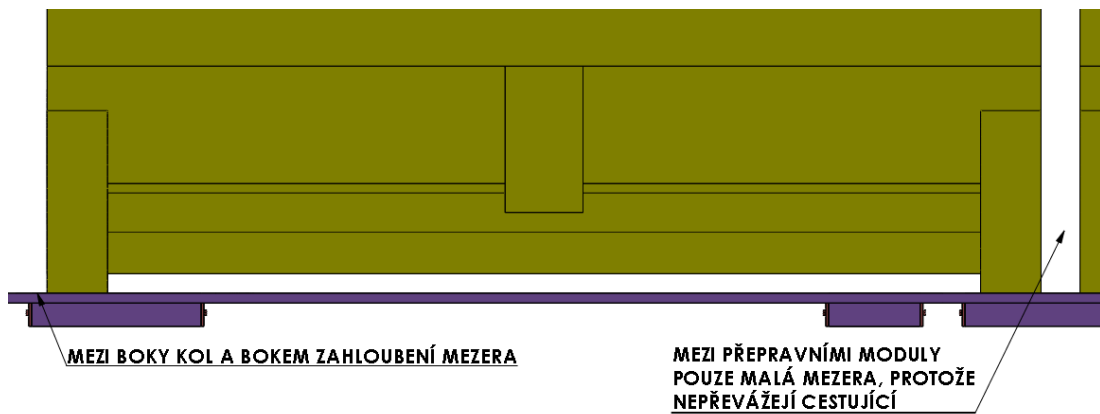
Hrubá stavební struktura - detail boku zabloubení
